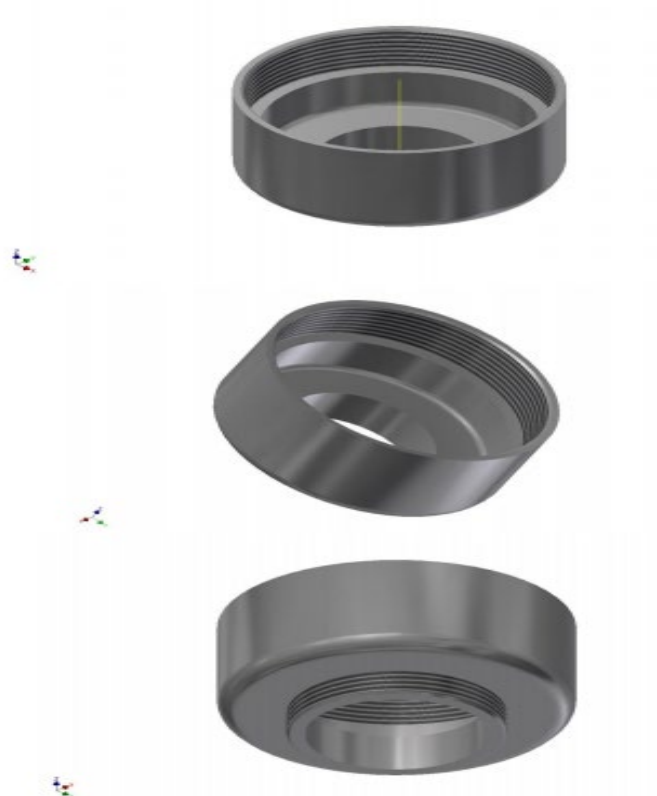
3D модель корпусу розливного пристрою.
